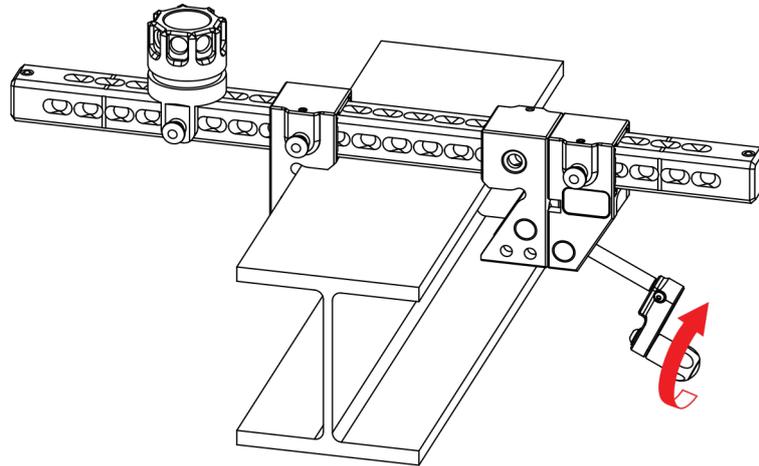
Instalación de Abrazadera de Viga I Paso 3
